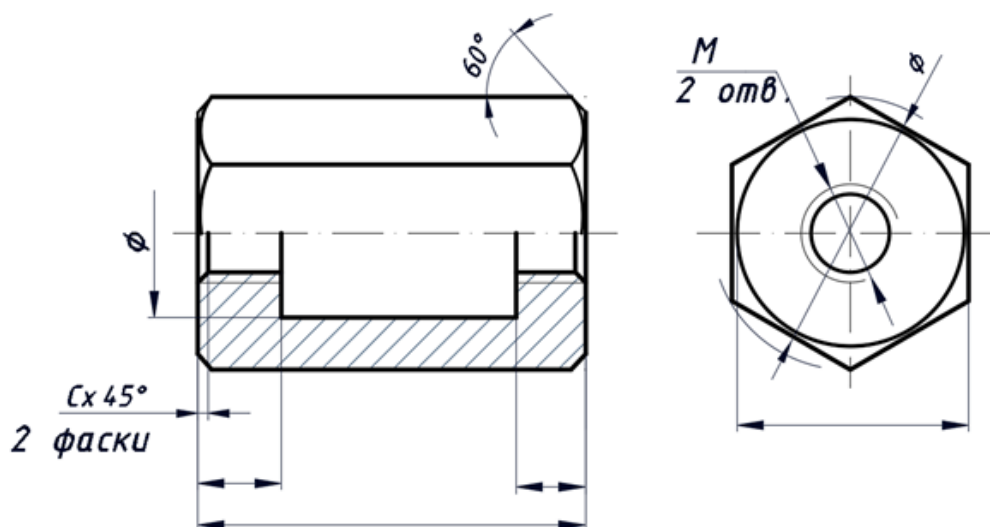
Образец выполнения чертежа детали, выполненный совмещением части вида и части разреза.
